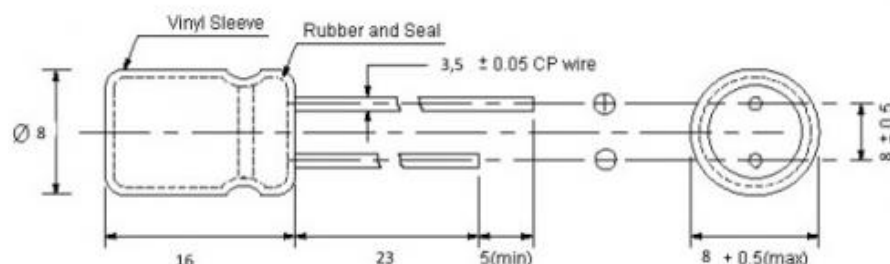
Габаритні розміри конденсатора типу ЕСАР
